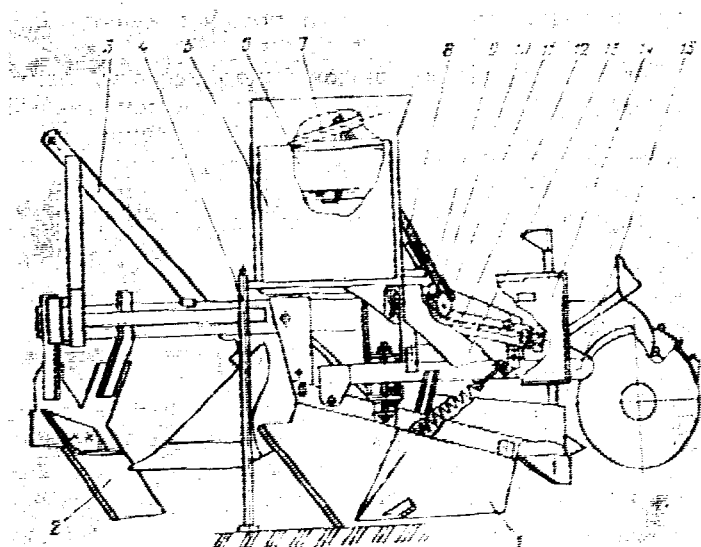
Приспособление лесопосадочное автоматическое ПЛА-1: 1 — сошник; 2 — нож черенковый; 3 — плуг лесной ПКЛ-70; 4 — стойка; 5 — ограждение; 6 — ящик; 7 — валик; 8 — механизм подачи; 9 — кассета; 10 — механизм лентопотяжной; 11 — корпус; 12 — вал промежуточный; 13, 14 — бункер; 15 — аппарат посадочный
